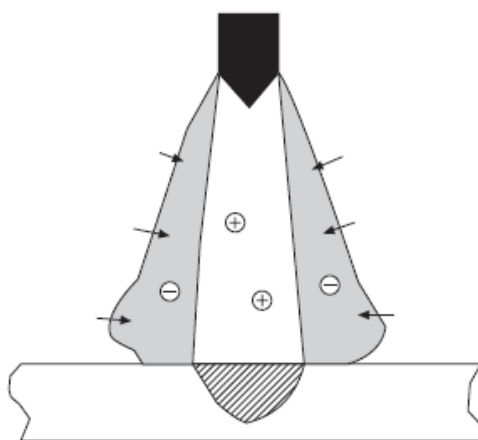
Constrição do arco elétrico em soldadura A-TIG
